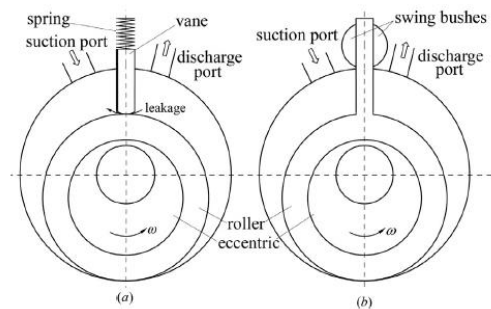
Vista corte de secção compressor de pistão rolante (a) e oscilante (b) [13]
